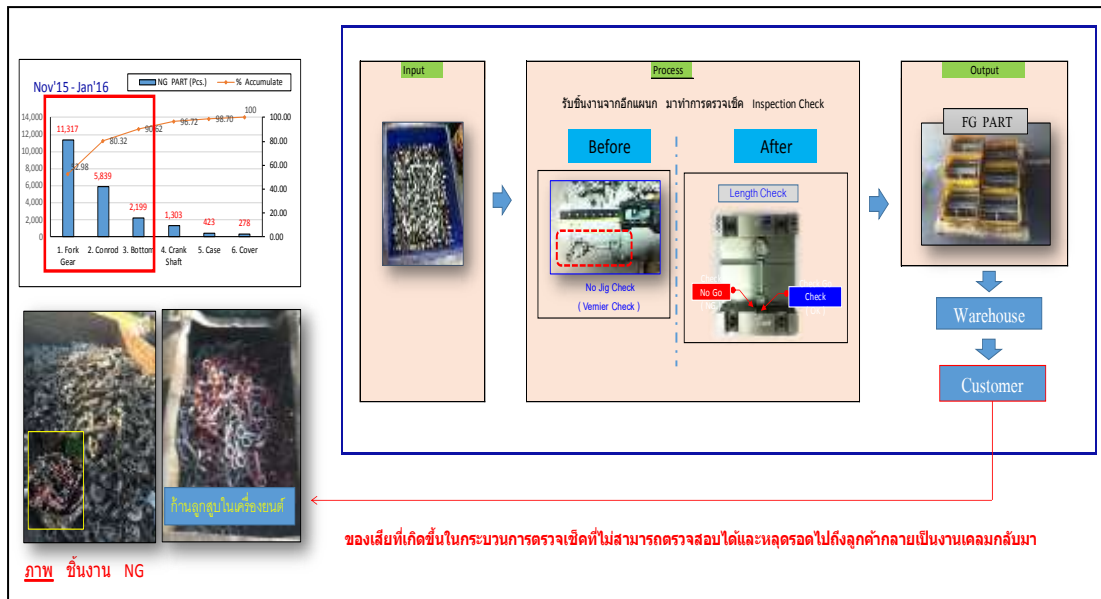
Jig check ระยะ Center model: fork gear
